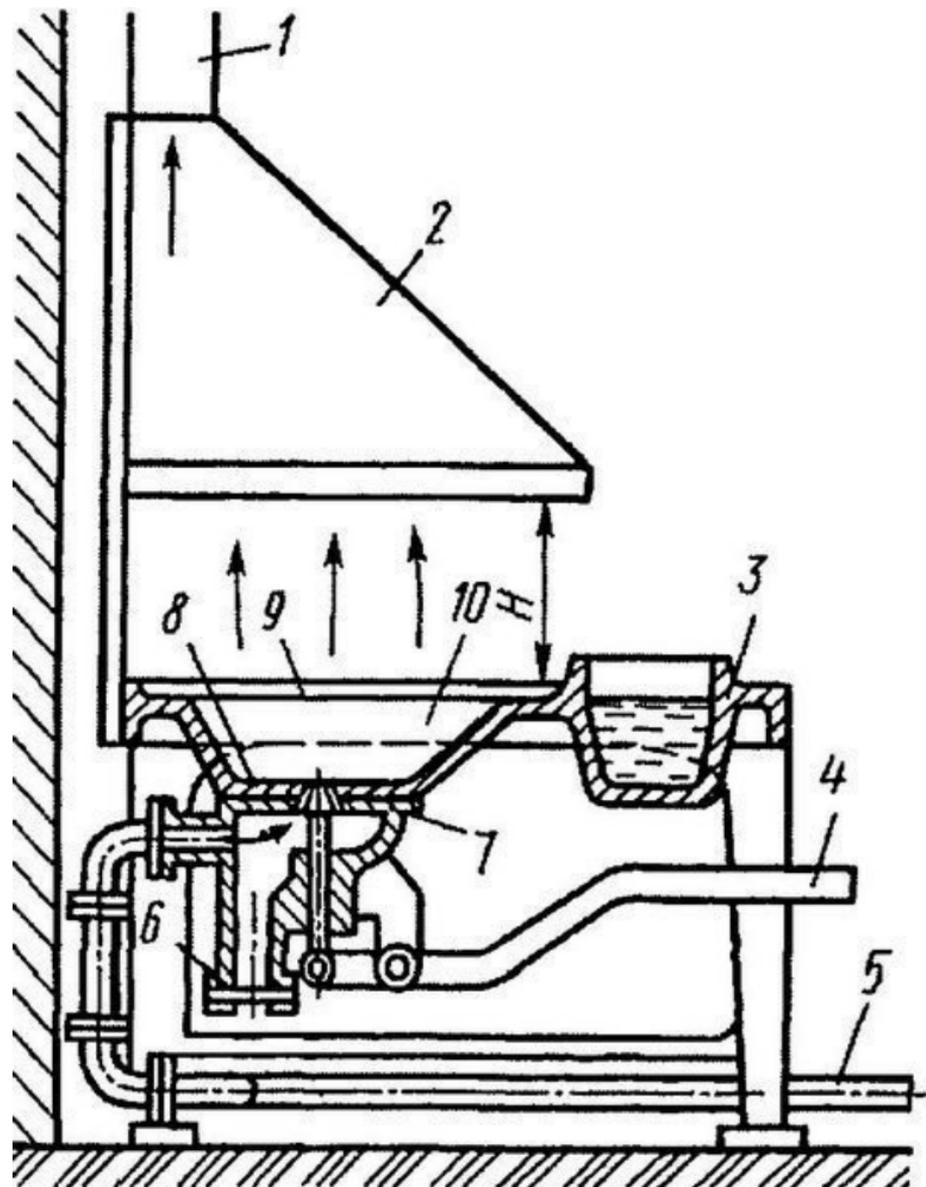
Стационарный горн с литым постаментом: 1 – вытяжная труба; 2 – зонтик; 3 – бачок с водой для охлаждения инструмента; 4 – рычаг для регулирования подачи воздуха; 5 – воздухопровод; 6 – заслонки; 7 – конический запорный наконечник; 8 – фурма; 9 – литой стол; 10 – очаг.
